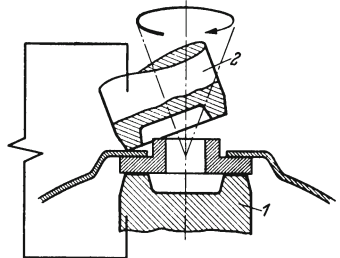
Torkelnahschweißmaschine. Die Ringnaht eines Stutzens wird zwischen der feststehenden Elektrode 1 und der Torkelektrode 2 geschweißt, die sich um einen Kegel auf der Naht abwälzt.
